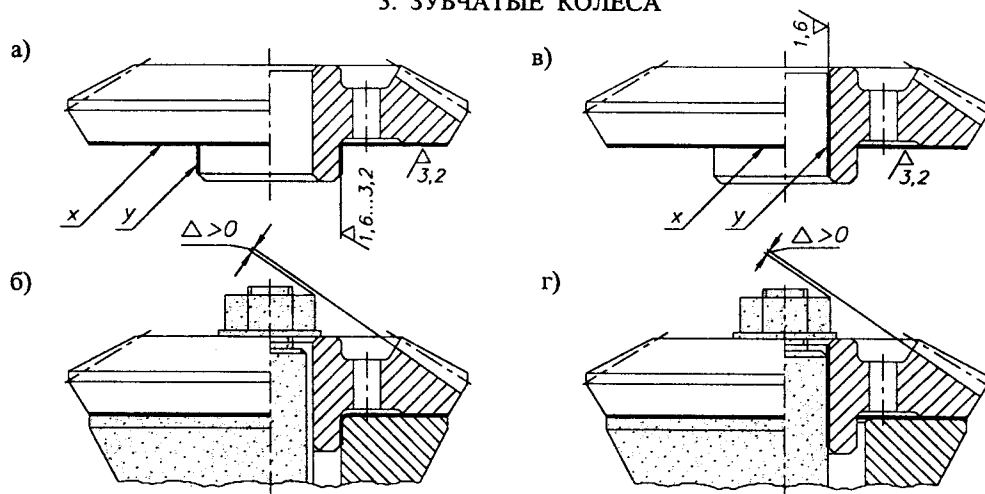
Установочные базы для нарезания зубьев на зубчатых колесах
